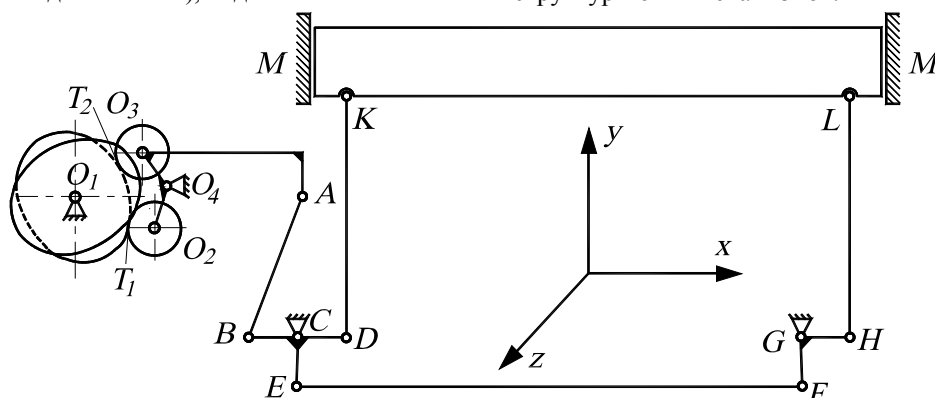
Кинематическая схема зевобразующего механизма станка Р-1-190
